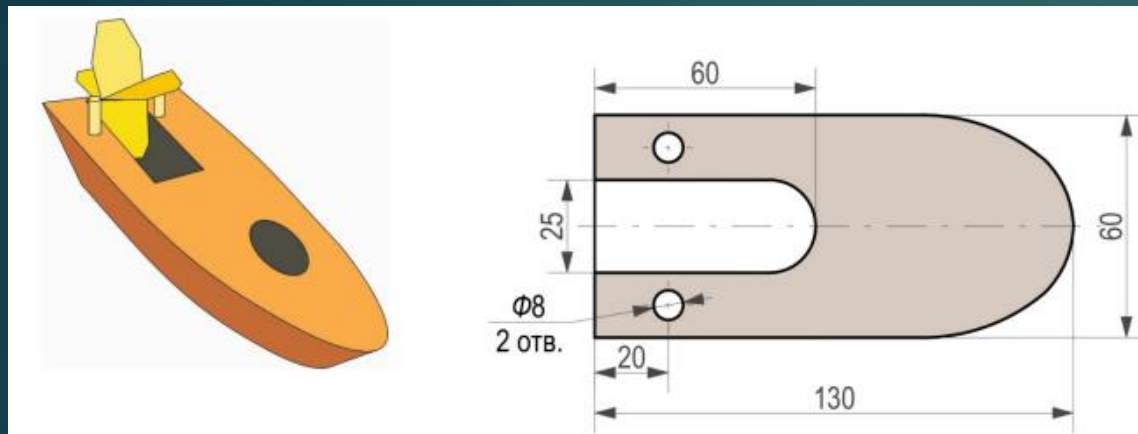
Вариант образца изделия детской игрушки «Лодочка»
